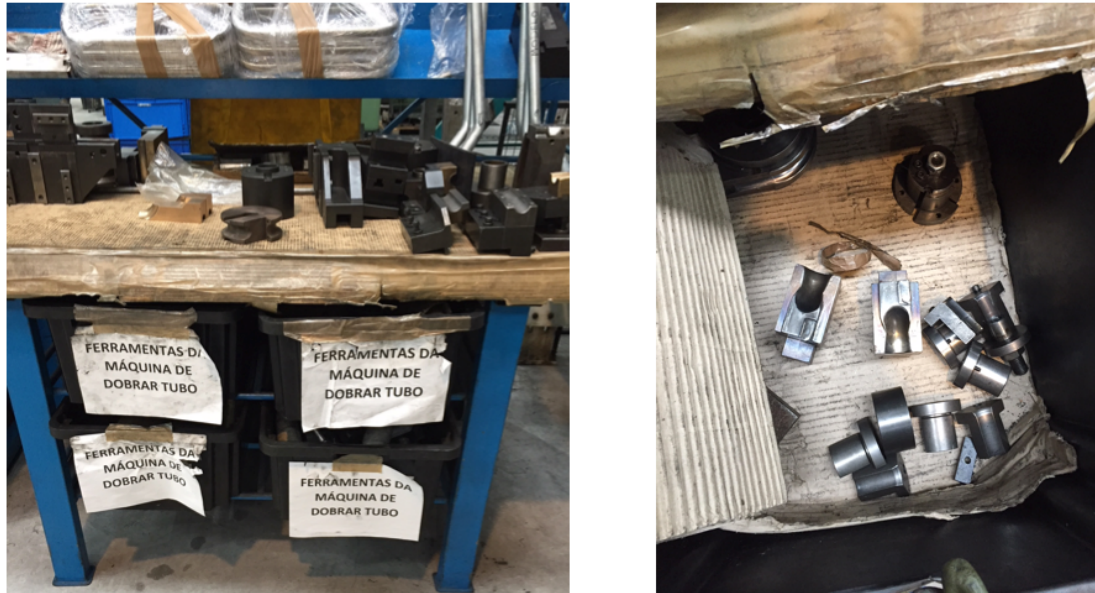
Espaço inicial das ferramentas da máquina de dobrar tubo
